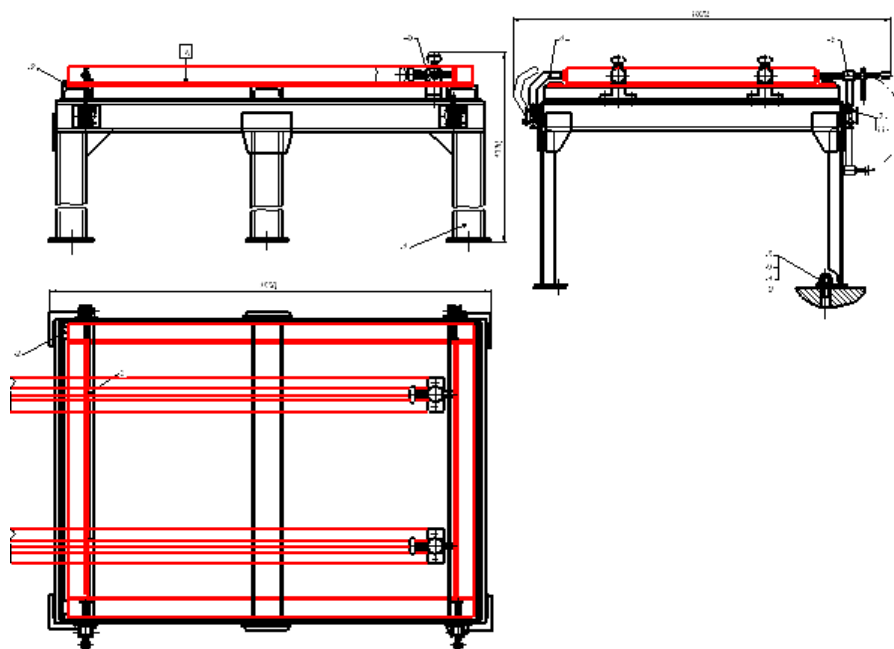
Сборочно-сварочный стол Forster
